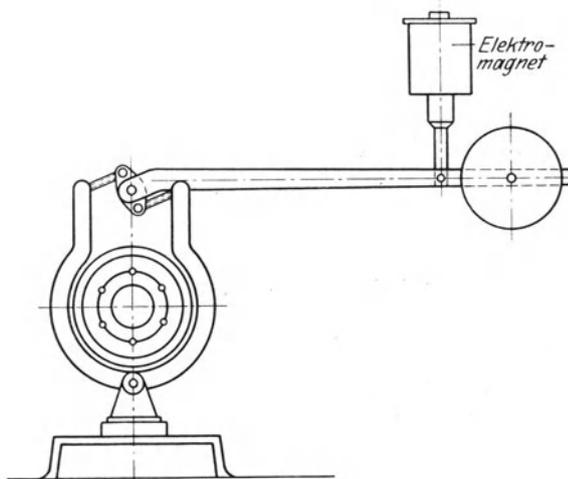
Elektromagnetisch gesteuerte Gewichtsbackenbremse.
